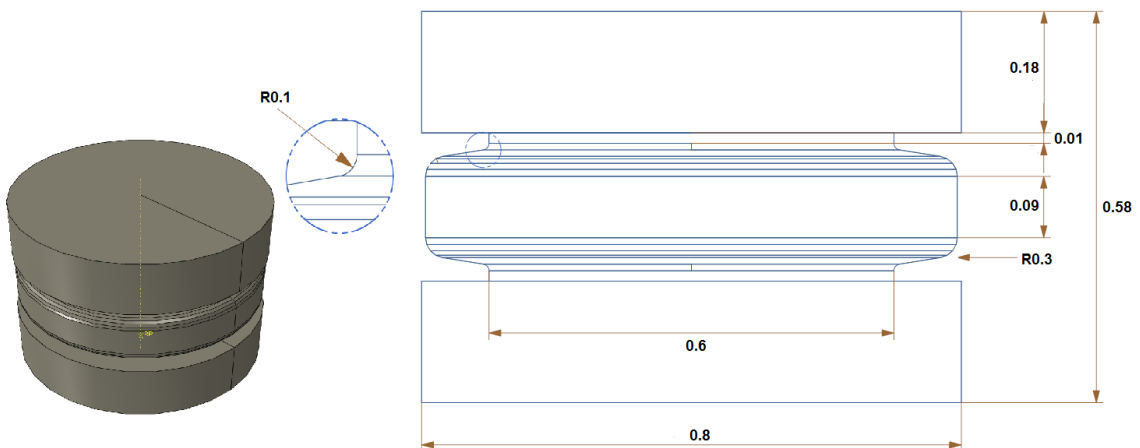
Geometría del rodillo 3, dimensiones en [m].
